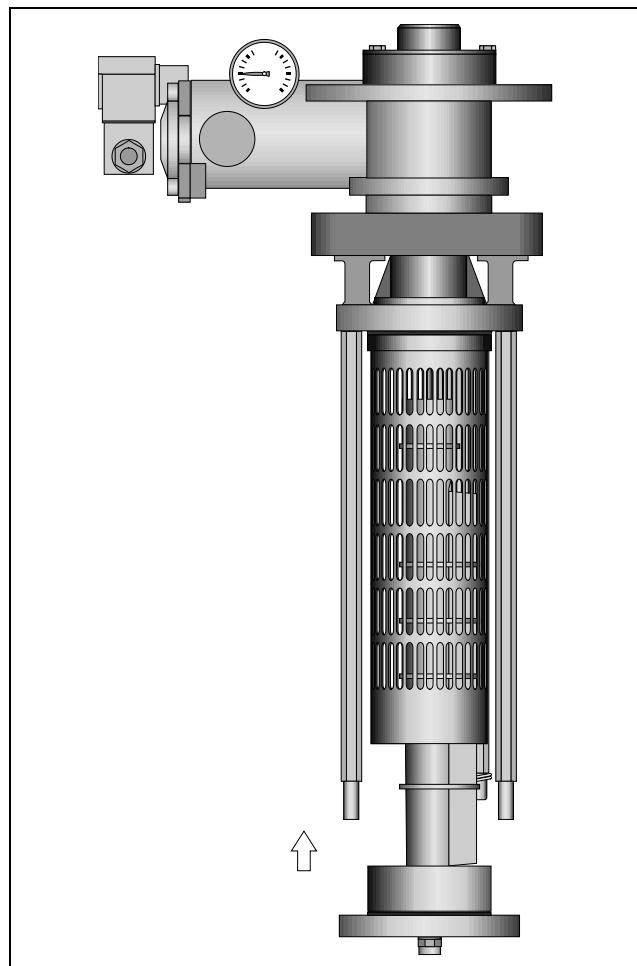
Vormontierte Baugruppe in Filterelement einbauen
